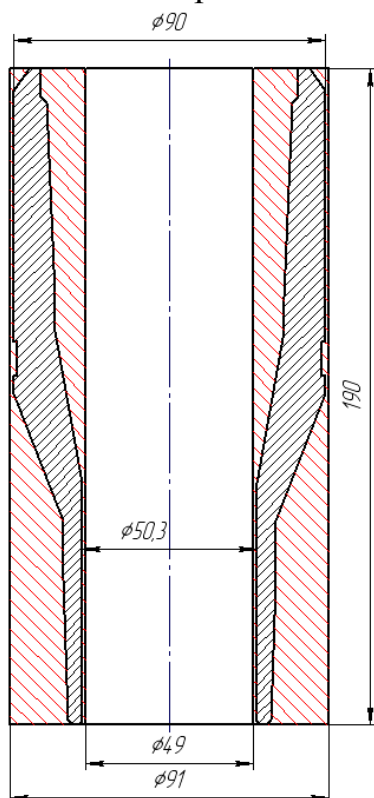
Соотношение объёмов припуска и готовой детали при изготовлении переводника П73/60 механообработкой
